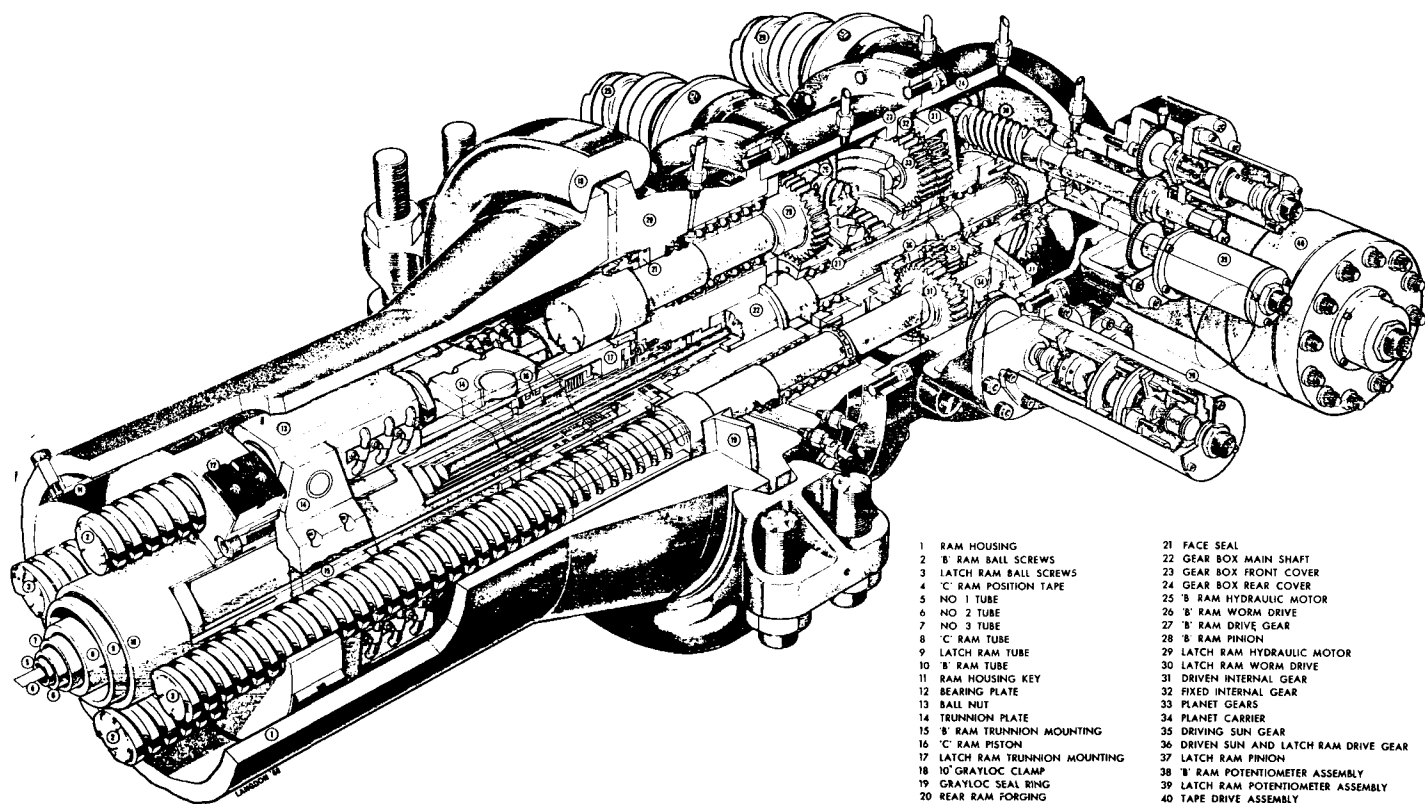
ESQUEMA DE LA PARTE POSTERIOR DEL MECANISMO DE EMPUJE
